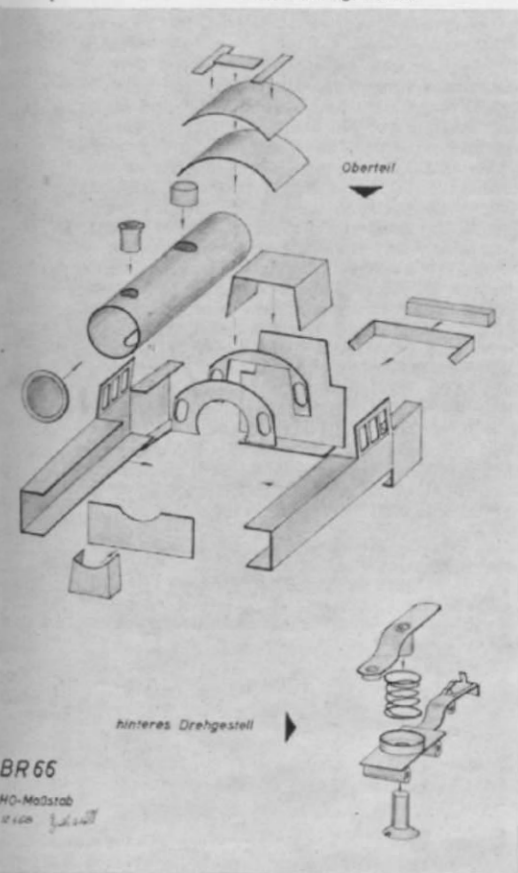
Explosionszeichnung des Verfassers für den Auf- und Zusammenbau des Lokgehäuses.
